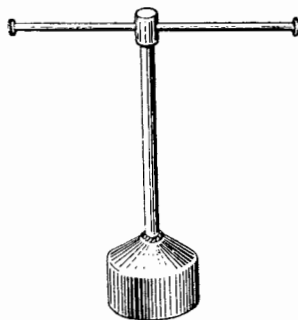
Ключ 47001-1-012МД для регулировки осей вилок переключения дет. 212-102 коробки передач
